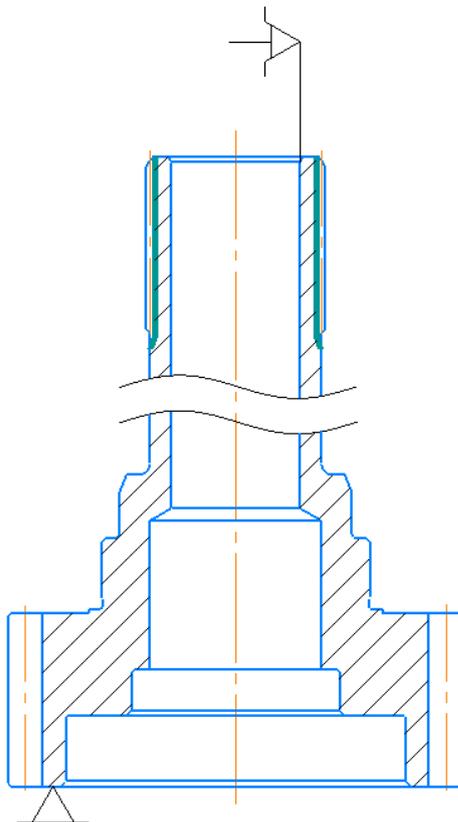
Схема закрепления детали на операции 060 Шлицефрезерная
